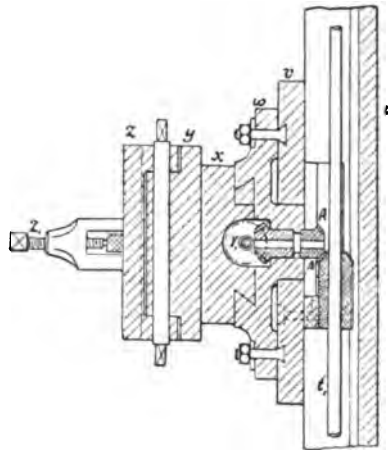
Horizontalschnitt des Supports einer Metallhobelmaschine.
